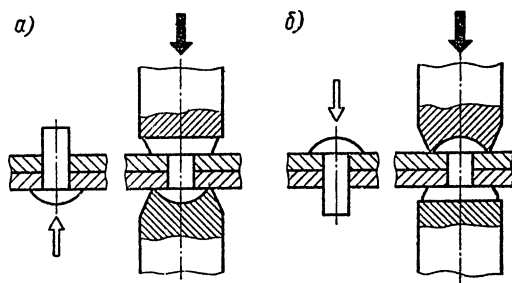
Прямой (а) и обратный (б) методы образования заклепок
